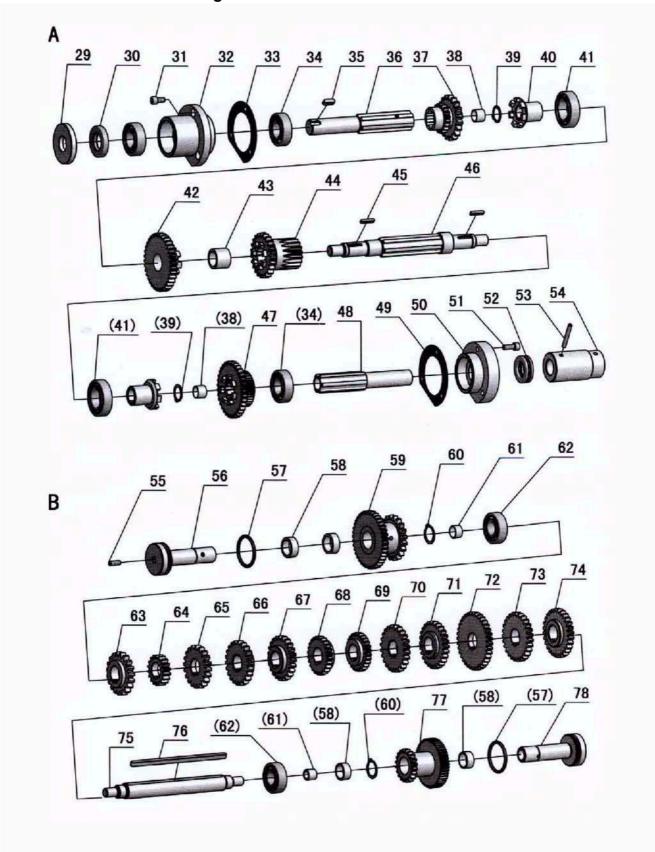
Vorschubgetriebe 2 von 4 - Headstock feed gear 2 of 4
